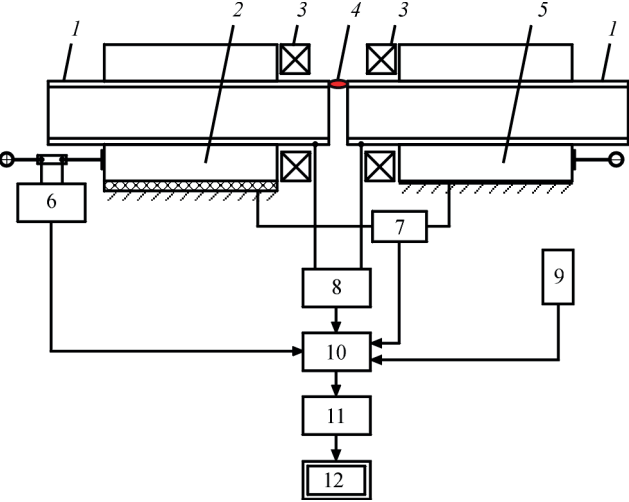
Блок-схема макету оцінки якості зварюваних з'єднань: 1 – зварювані труби; 2 – рухомий затискний пристрій; 3 – елементи магнітної системи; 4 – стовп електричної дуги; 5 – нерухомий затискний пристрій; 6 – датчик струму; 7 – датчик положення; 8 – датчик падіння напруги на зварювальній дузі; 9 – датчик вимірювання абсолютного тиску гідравлічної системи; 10 – нормуючий інструментальний підсилювач (з ФНЧ  $F_{зр} = 100$  Гц); 11 – приймаючий АЦП; 12 – промисловий комп'ютер
